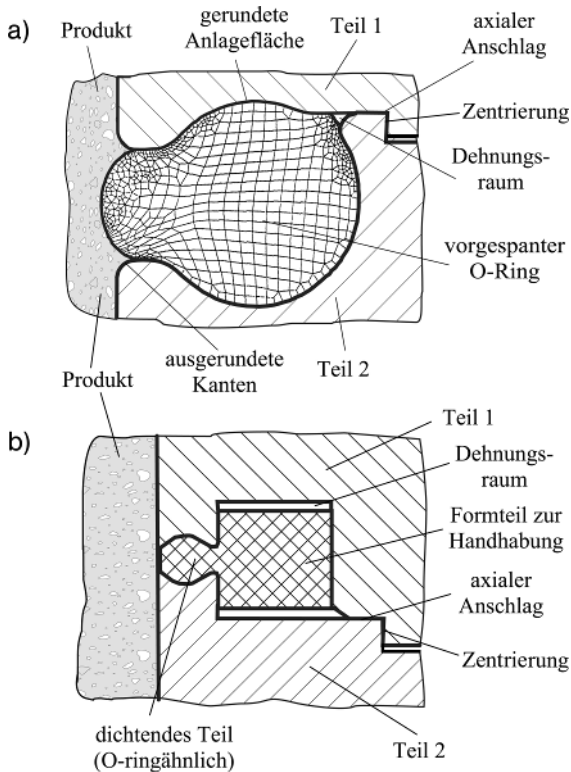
Optimierte hygienegerechte O-Ring-Abdichtung mit axialem Anschlag und Zentrierung nach DIN 11 864 [62]:
